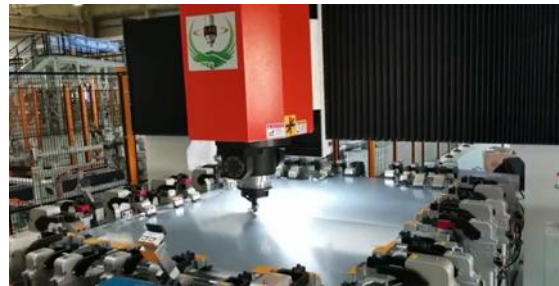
电池托盘搅拌摩擦焊焊接夹具结构
